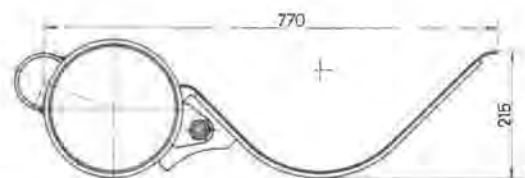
Assemblage du tube au couloir en « demi-lune ».
